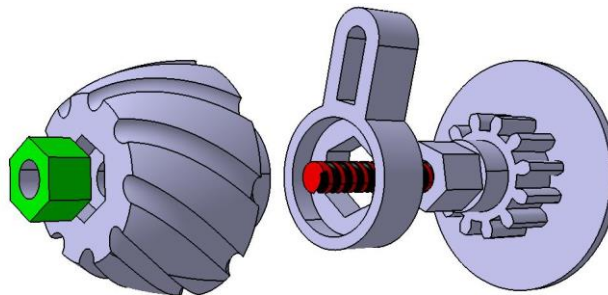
Conjunto para fijar, o girar, el engranaje.
